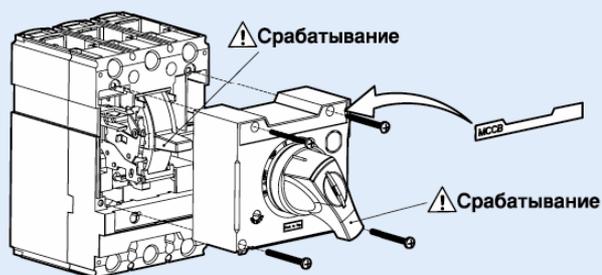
Габаритные и установочные размеры, способ установки стандартных поворотных ручек TD100 - TD160
